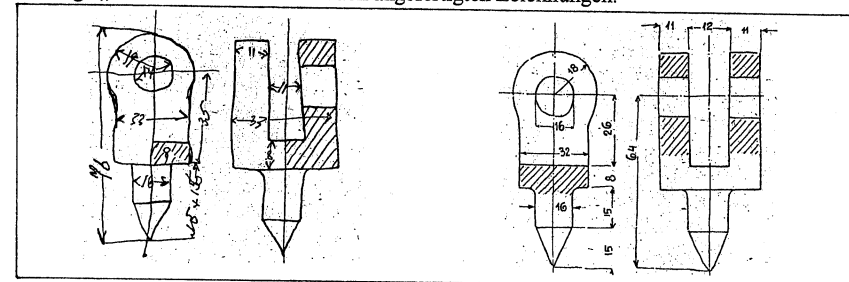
/10: Skizze und Zeichnung eines Zapfengelenks (um 1920)
